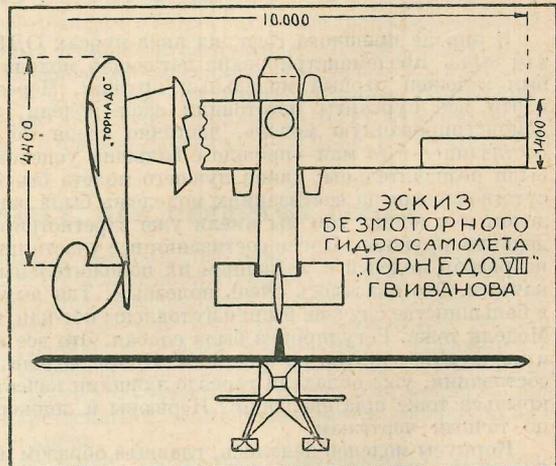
Схема гидропланера конструкции Г. Иванова.
